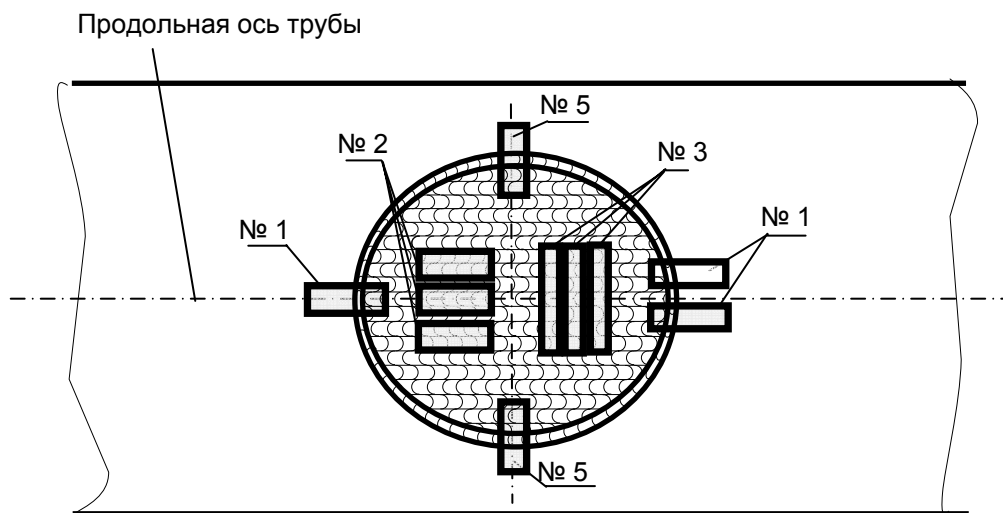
Схема вырезки образцов для проведения механических испытаний при аттестации технологии ремонта сваркой (наплавкой) с круглой (овальной) выборкой:
